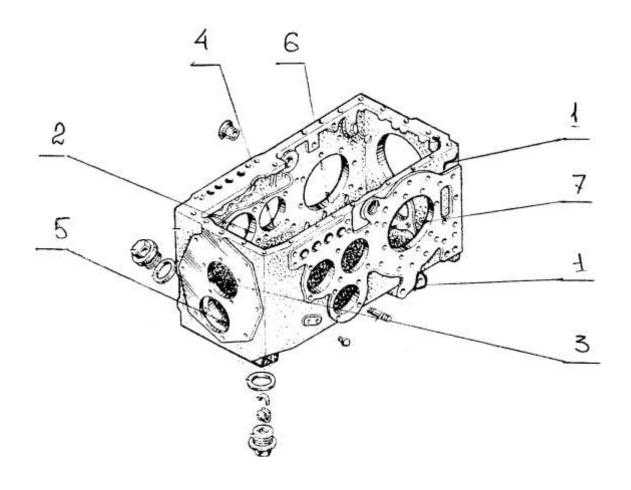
Основные дефекты корпуса заднего моста трактора T-25.
